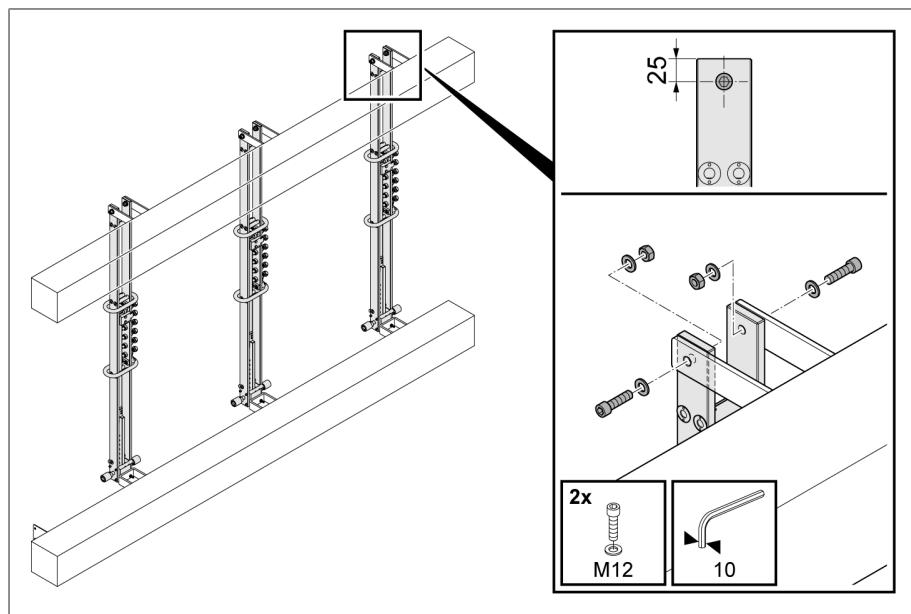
Крепление держателя, устройство ПБВ с боковым расположением контактов
